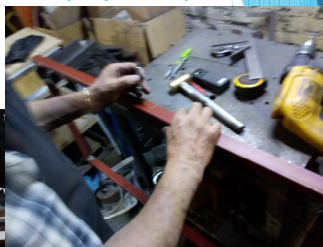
Soldado de marco soporte para Construcción de equipo colateral
